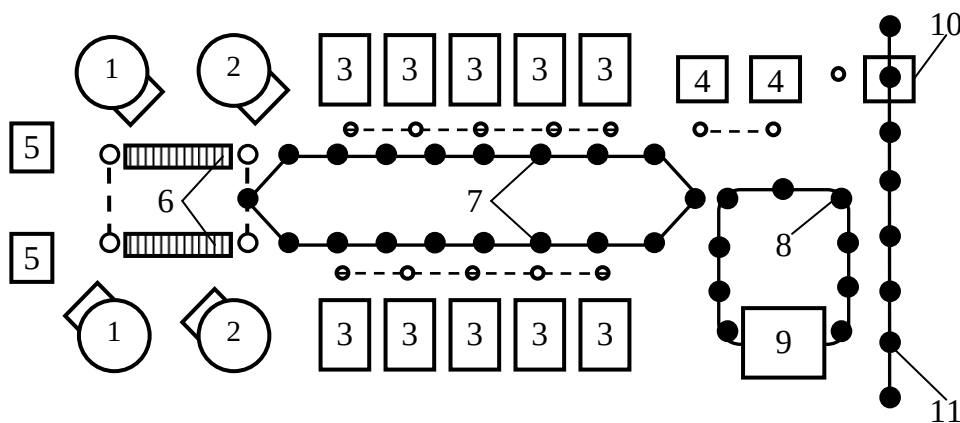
Схема планировки оборудования поточной линии для обработки зубчатых колес:
